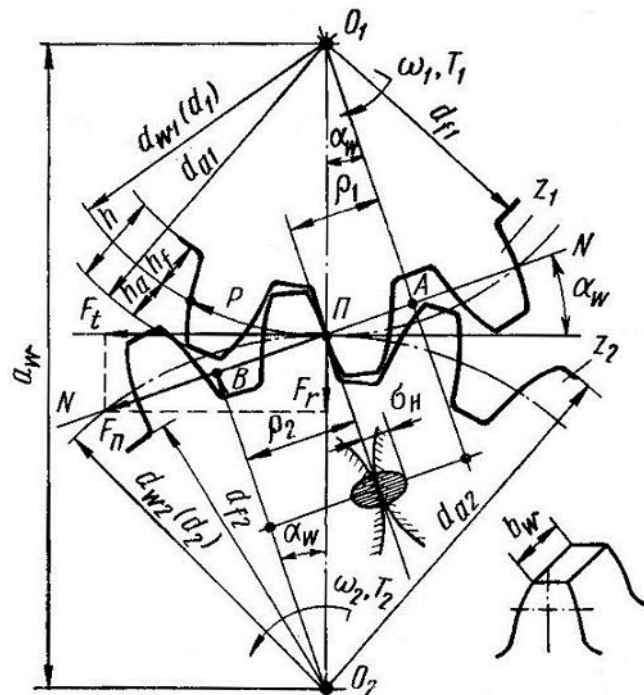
Схема зацепления двух зубчатых колес
